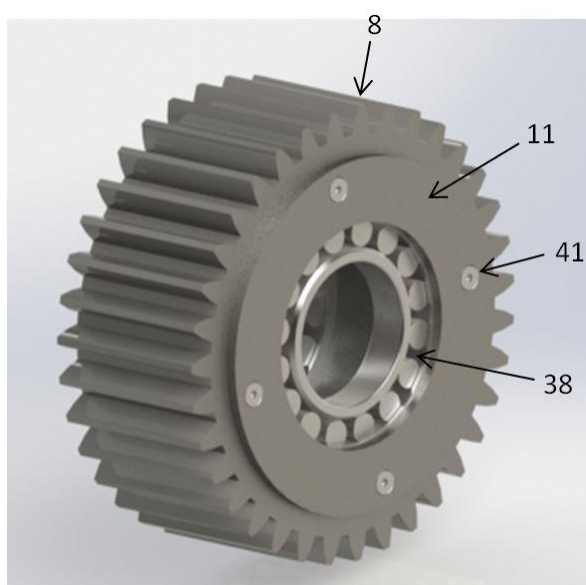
Planeta do primeiro estágio de multiplicação preparado
